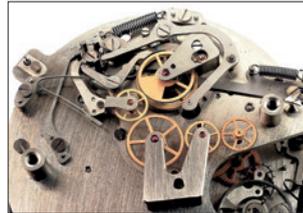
»60 ЧП« mit 2 Spiral-Federn
